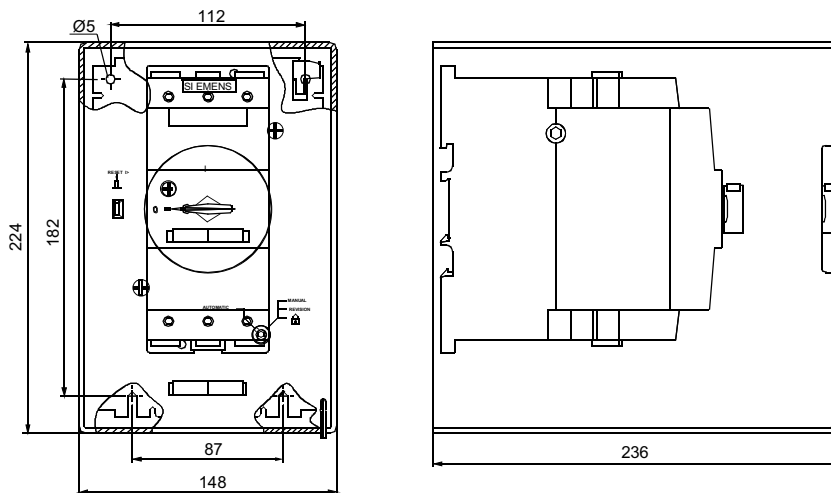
Motor-Fernantrieb 3RV1946-3A
